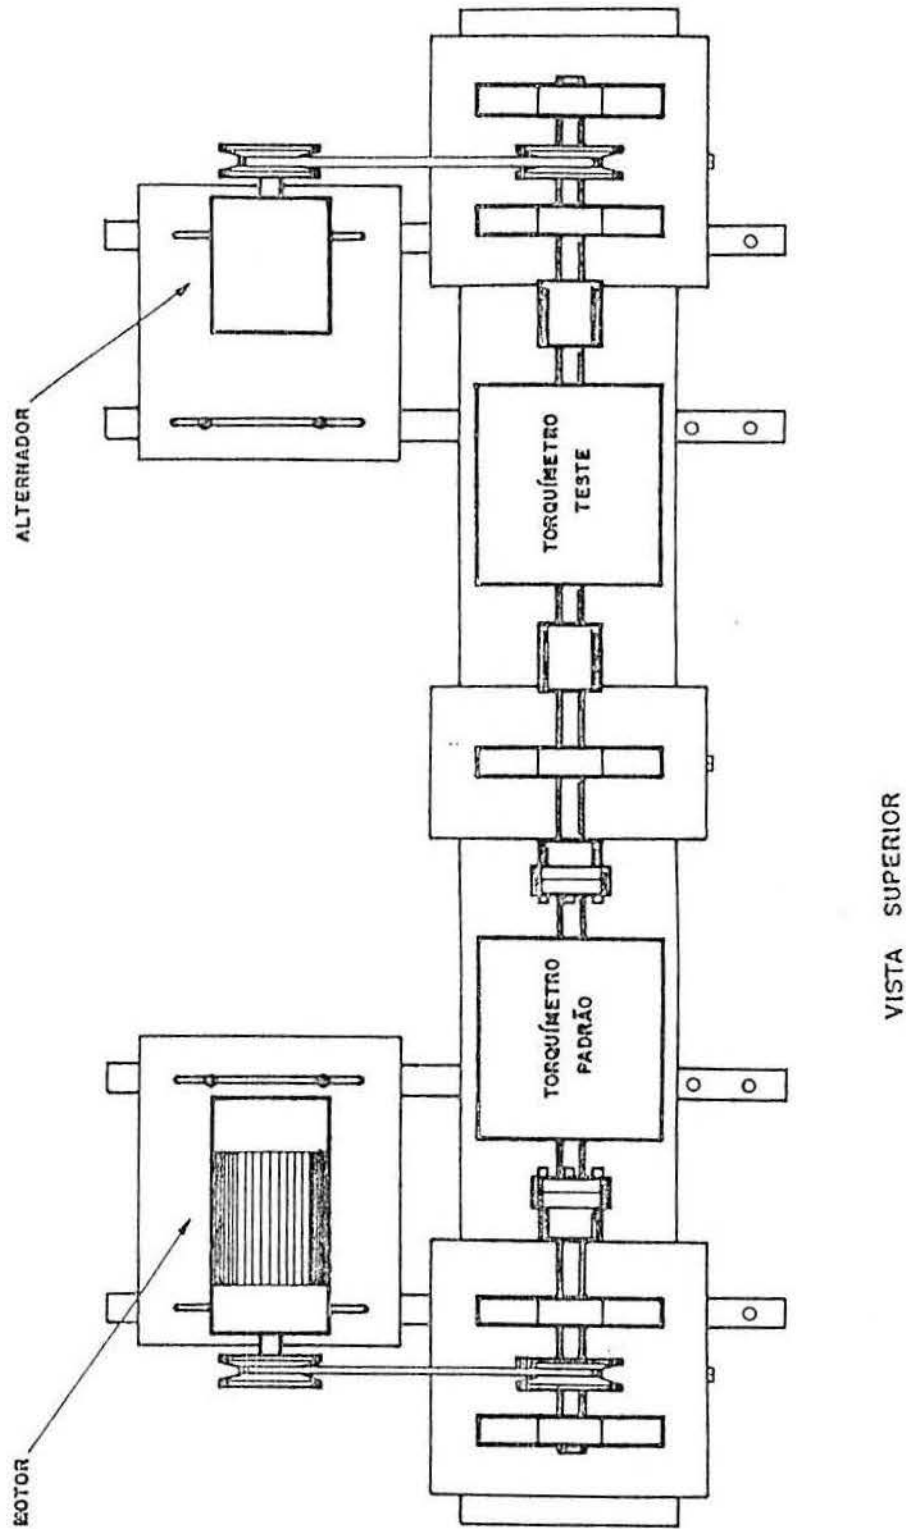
Vista superior do conjunto, com motor, alternador e torquímetros
